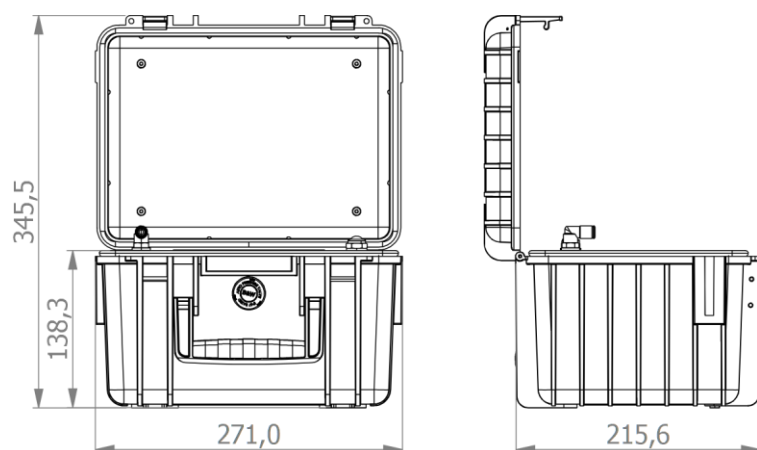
Dimensioni OIL CHECK 500 | versione mobile
